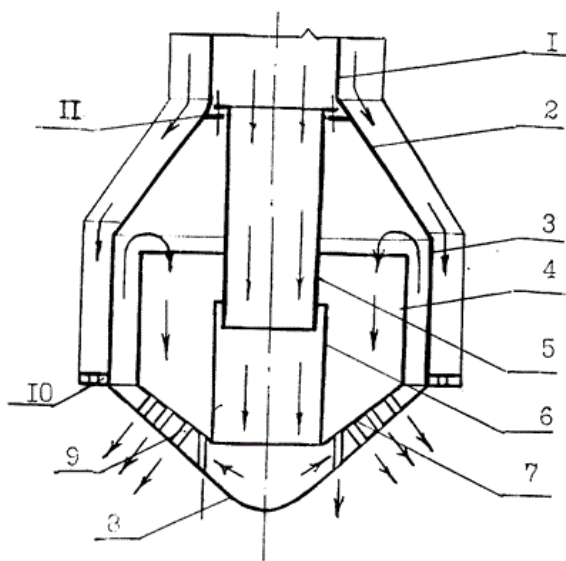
«Смеситель конвертора метана: 1 - патрубок подвода смешиваемого газа, 2 - раструб, 3 - цилиндрическая обечайка, 4 - стакан наружный, 5 – верхний стакан, 6 – нижний стакан, 7 - коническая обечайка, 8 - днище, 9 - форсунки, 10 - кольцевая решетка, 11 - кольцо для закрепления верхнего стакана газоведа» [10]
